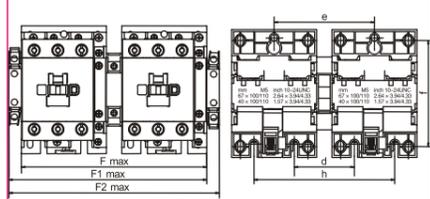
Габаритные и установочные размеры контакторов с реверсивной сборкой на токи 40А-95А, мм.
